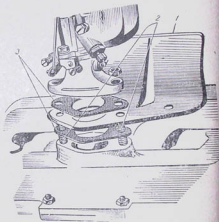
Крепление и установка козырька выхлопной трубы:
